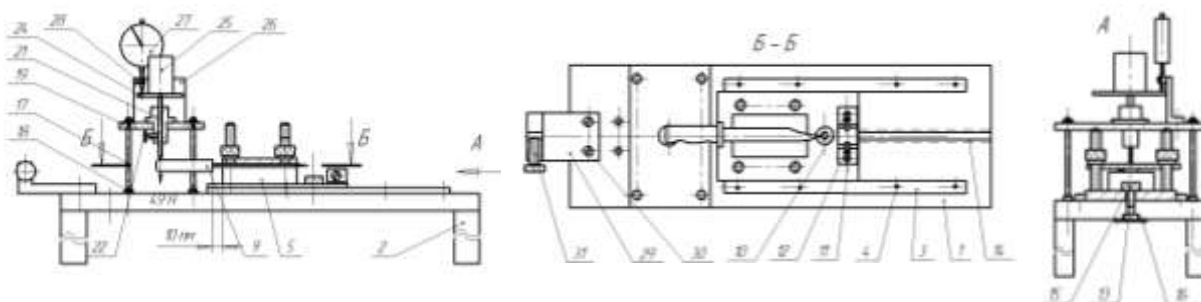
Схема налагодження пристрою для визначення міцності конструкції вузла з'єднання клинка з руків'ям: 1 – корпус; 2 – ніжки; 3 – напрямні; 4 – гвинти; 5 – рухомий столик; 6 – шпильки; 7 – пластина; 8 – гайки; 9 – руків'я; 10 – опорний елемент; 11 – гвинт; 12 – гвинт регулюючий; 13 – болт стопорний; 14 – Т-подібний паз; 15 – гайка; 16 – пластина; 17 – стойка; 18 – гайка; 19 – пластина; 20 – гайка; 21 – напрямна; 22 – гвинт стопорний; 23 – вимірювальний штир; 24 – пластина; 25 – вага; 26 – опора; 27 – вимірювальний прилад; 28 – гвинт; 29 – кронштейн; 30 – гвинт; 31 – гвинт; 32 – різьбові отвори
